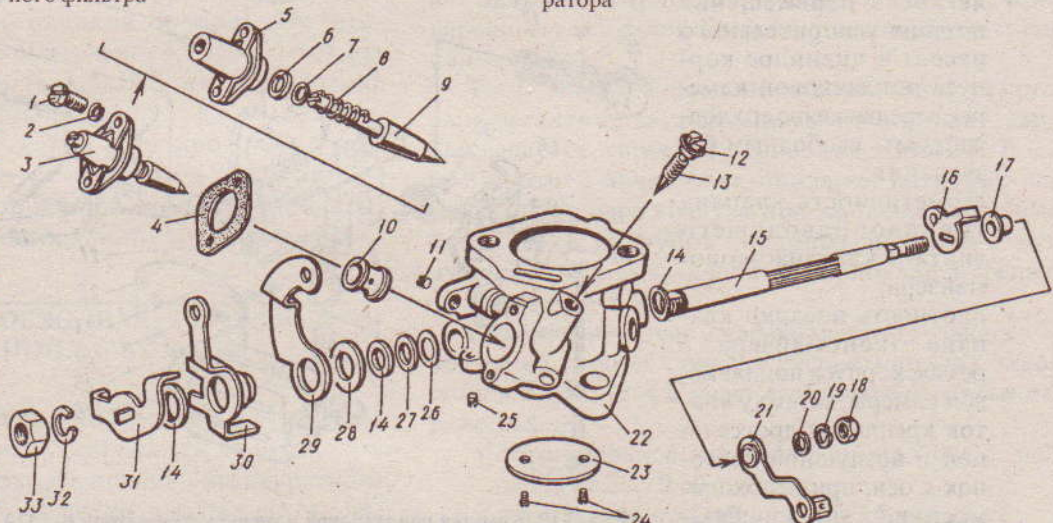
Корпус смесительной камеры карбюратора К-133А: 1 - винт М4; 2 - шайба; 3 - винт регулировочный; 4 - прокладка; 5 - корпус регулировочного винта; 6 - манжета; 7 - шайба опорная; 8 - пружина; 9 - винт регулировочный; 10 - распылитель; 11 - винт; 12 - кольцо 004-006-14-1-3; 13 - винт регулировочный; 14 - шайба; 15 - ось; 16 - рычаг промежуточный; 17 - втулка промежуточного рычага; 18 - гайка; 19 - шайба; 20 - шайба; 21 - рычаг; 22 - корпус смесительной камеры; 23 - заслонка дроссельная; 24 - винт М3; 25 - винт упора; 26 - шайба; 27 - шайба; 28 - шайба; 29 - рычаг малых оборотов; 30 - рычаг; 31 - рычаг; 32 - шайба; 33 - гайка
